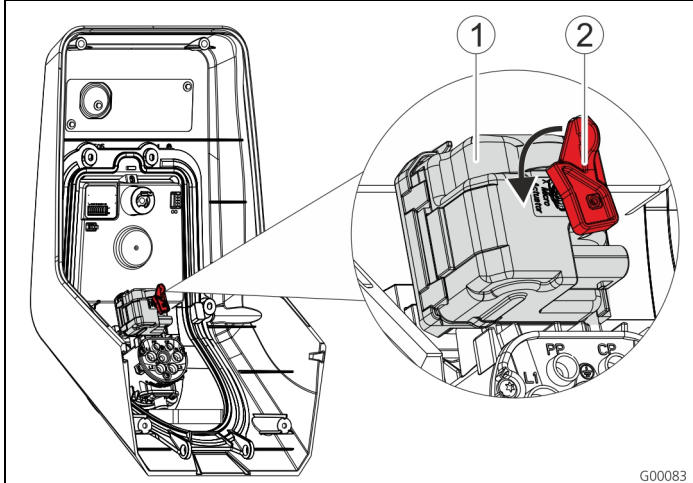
sbloccaggio d'emergenza della spina di ricarica
